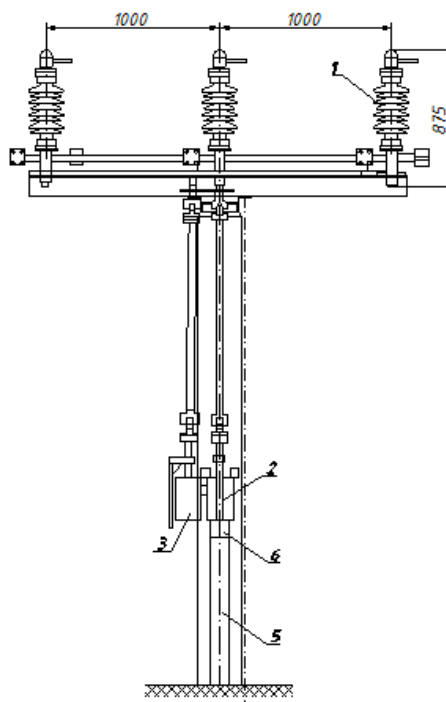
Конструктивный вид разъединителя РГП2–35/1000УХЛ1
